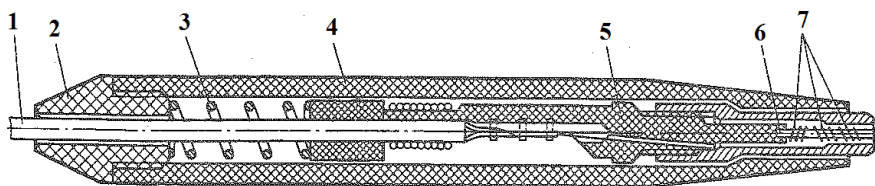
Накладной вихретоковый преобразователь карандашного типа с подпружиненной катушкой: 1 – кабель; 2 – колпачок; 3 – пружина; 4 – оправка; 5 – корпус; 6 – стержень; 7 – обмотки
